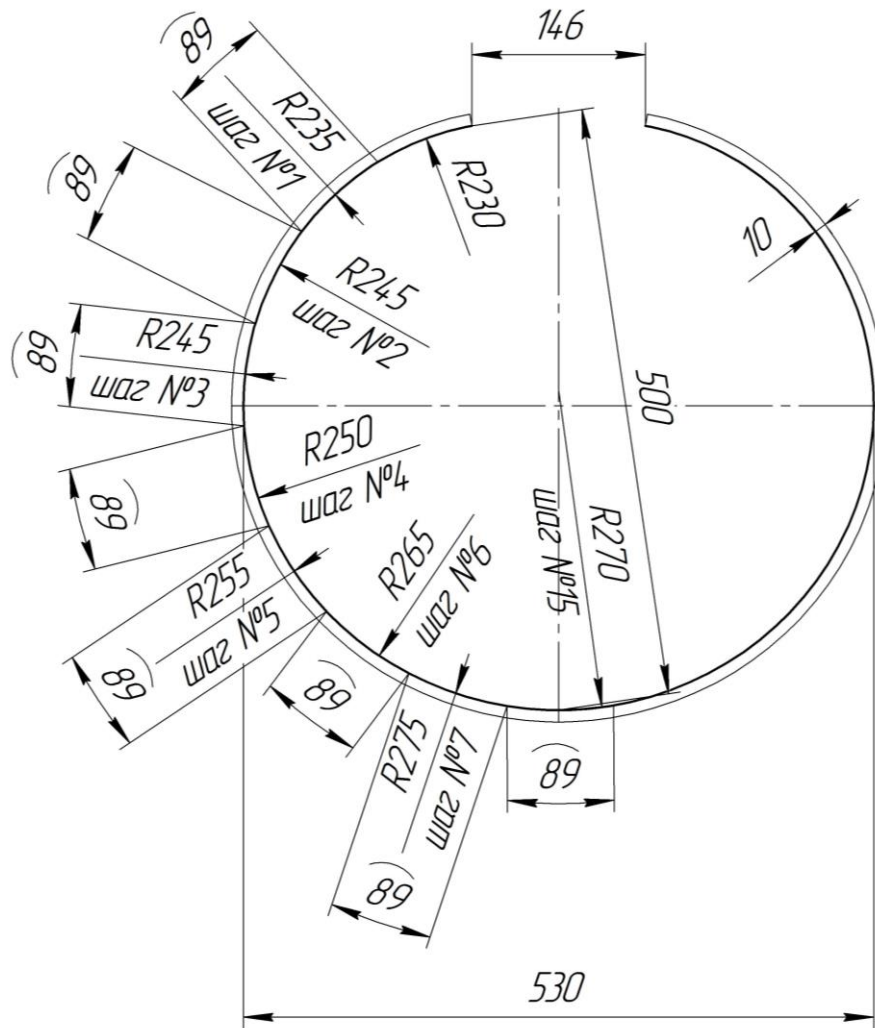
Схема профиля трубной заготовки для получения труб диаметром 530 мм с толщиной стенки 10 мм
